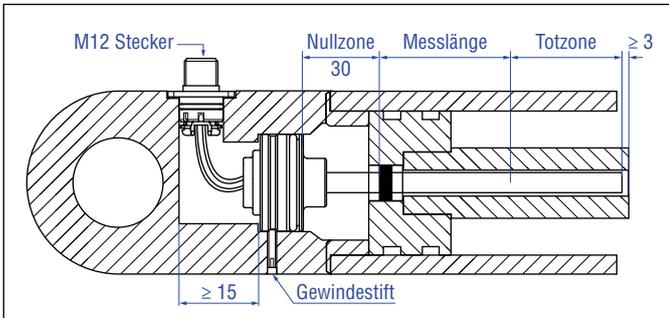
Beispiel für eine In-Zylinder-Montage mit M12 Stecker
